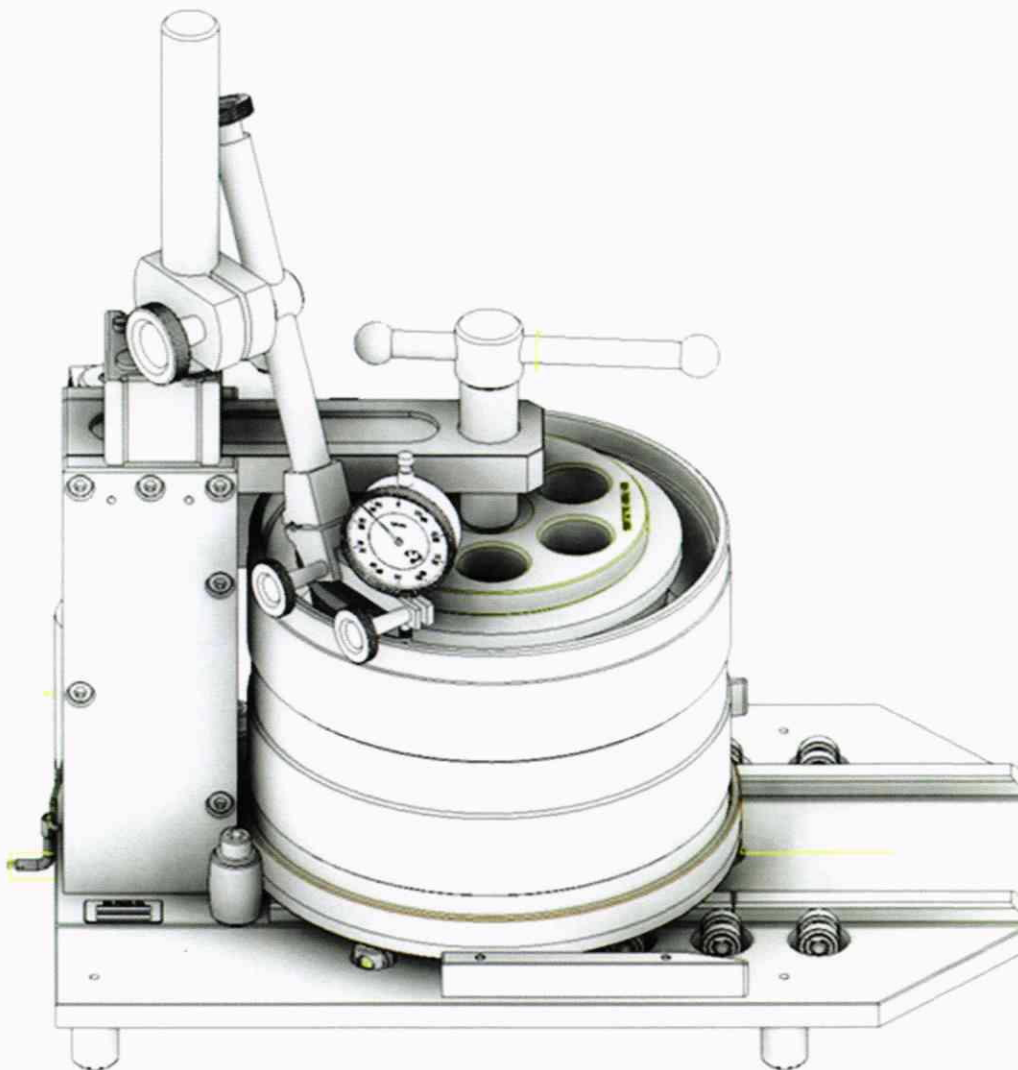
Схема установки индикатора часового типа 1МИГ 0-1
